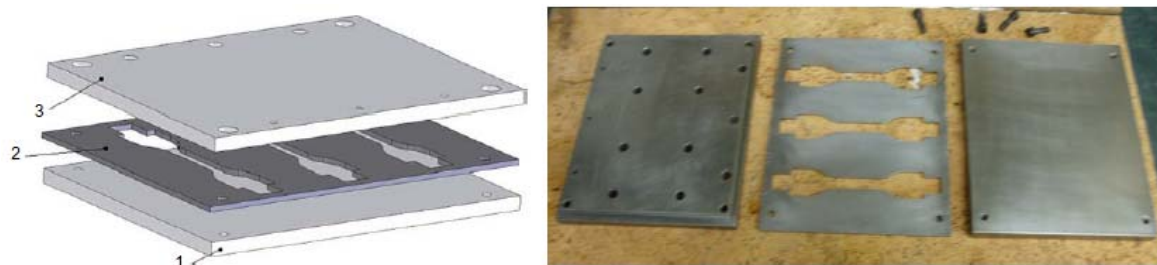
Molde de para fabricação de provetes em adesivo maciço [15, 22]
